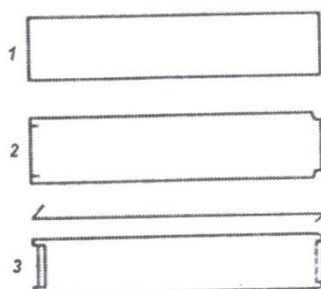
в. Послідовність обробки заготівлі корпусу:
